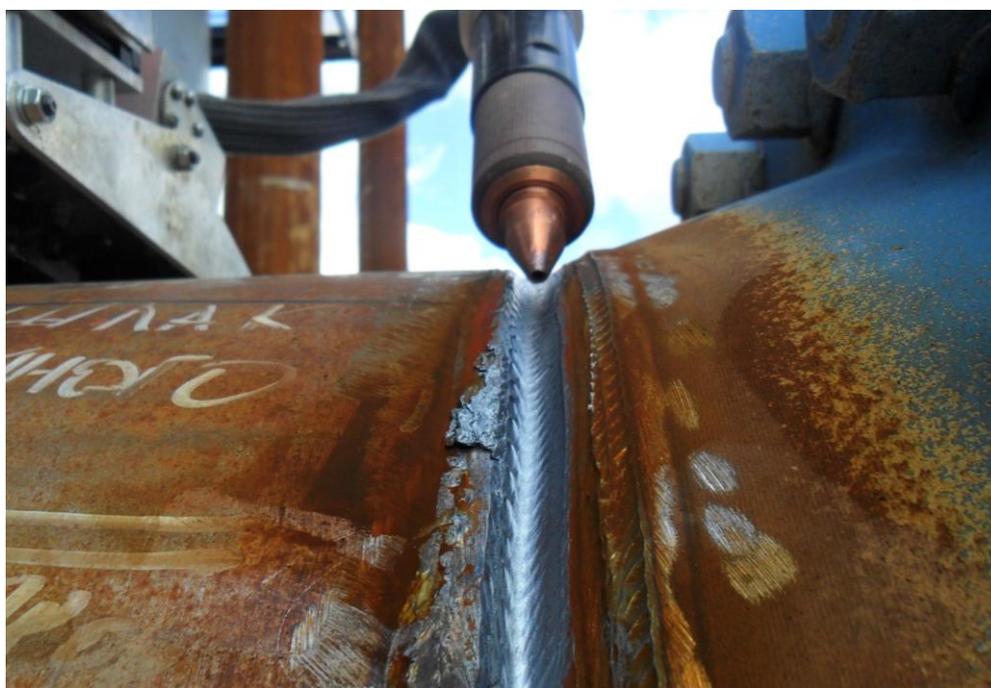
Выборка наплавленного металла в сварном шве
